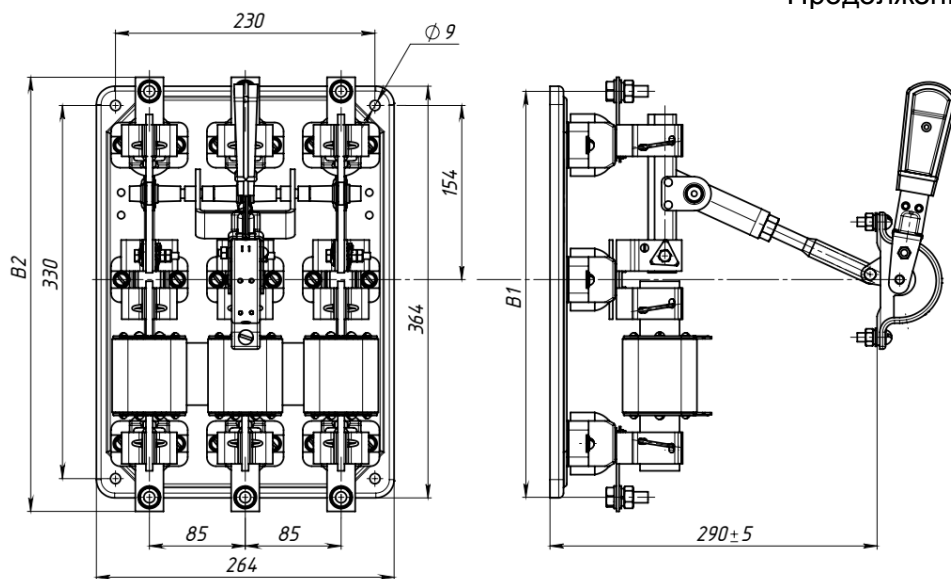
Б Разъединители-предохранители с боковой смещенной рукояткой на токи 1000 А и 1600 А, масса, не более: РПБ-10 – 26,35 кг; РПБ-16 – 29,3 кг.
